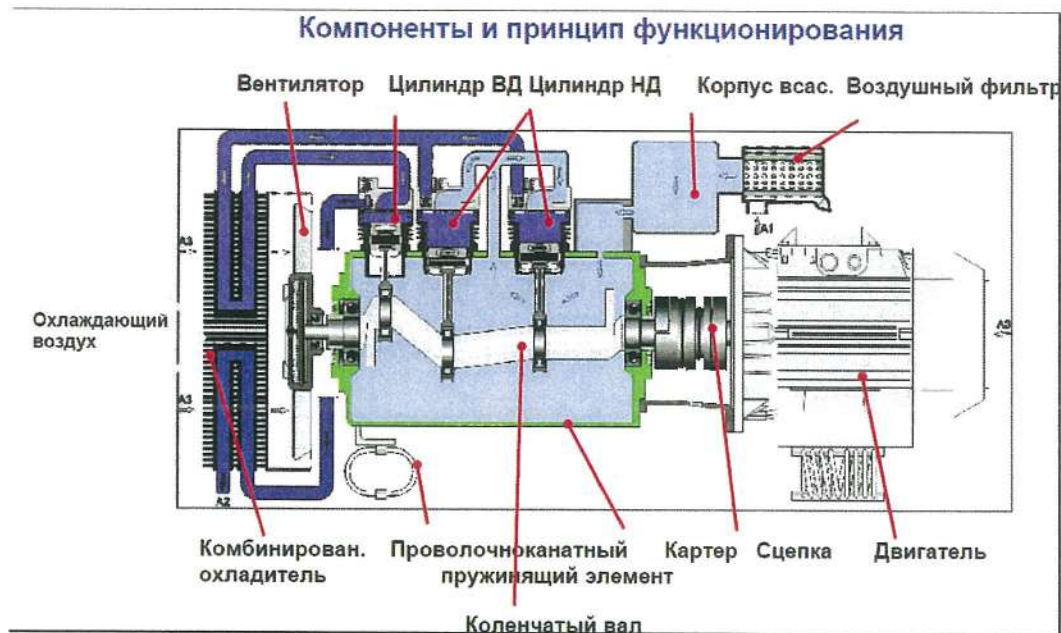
Безмасляный компрессорный агрегат типа «W-180T»
